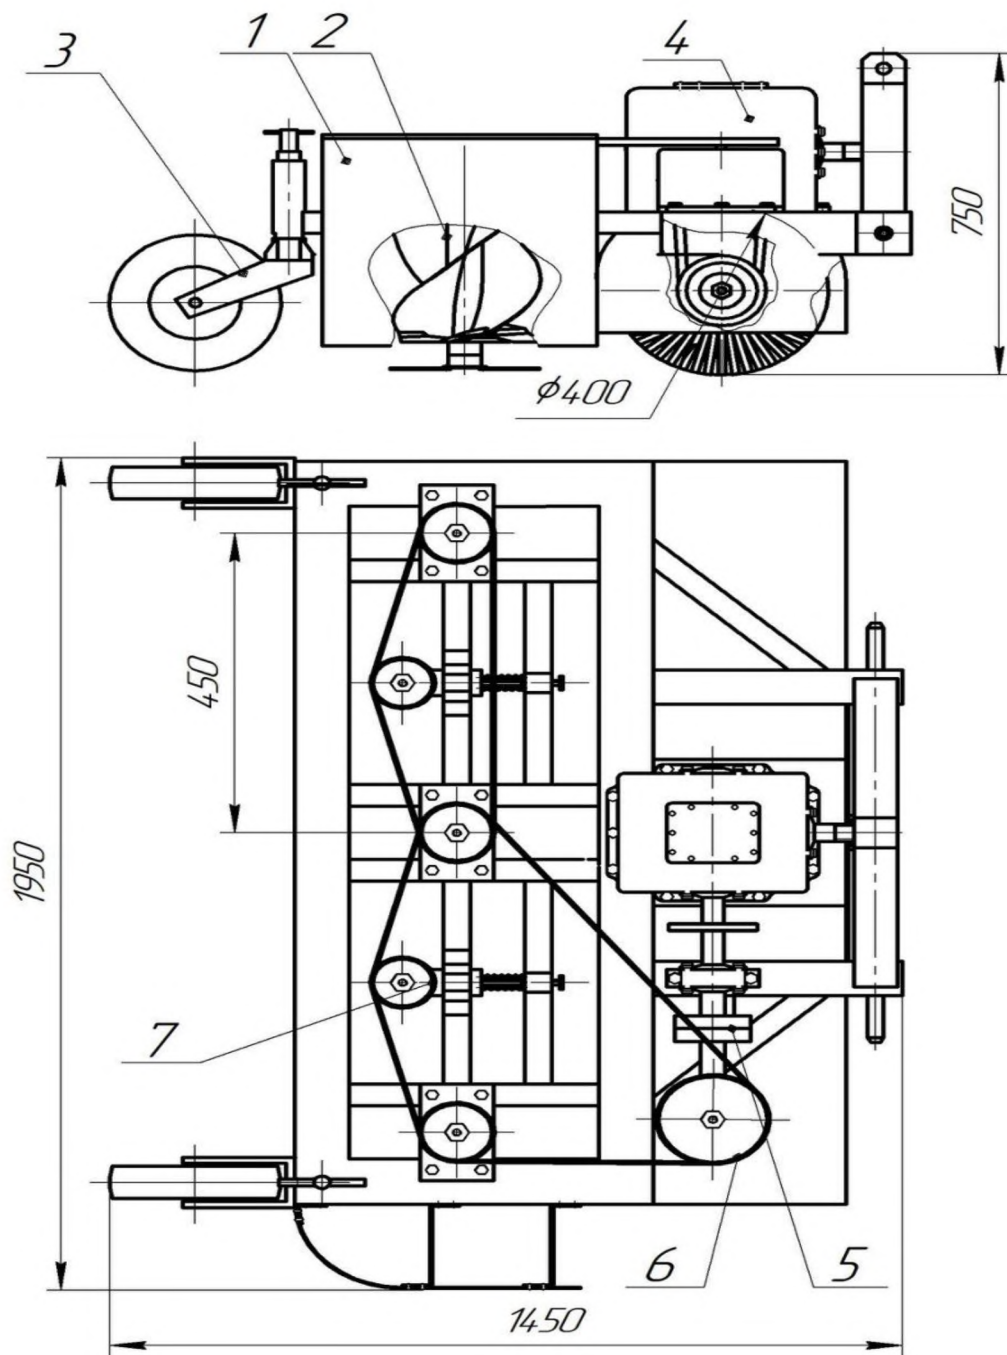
Принципова схема гичкозрізувального механізму
